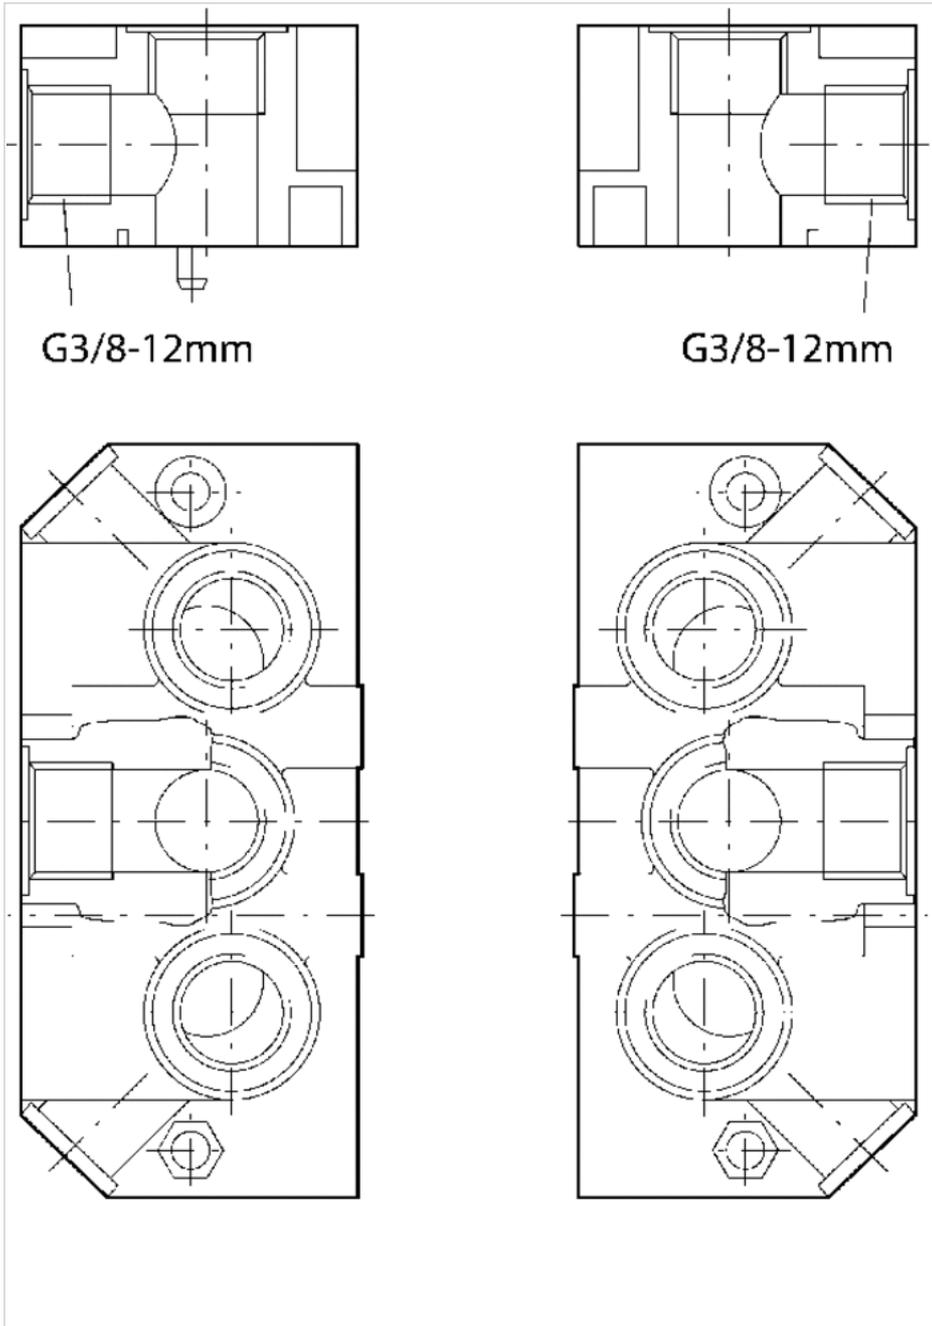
Gewindeanschlüsse 1 3 und 5 axial
